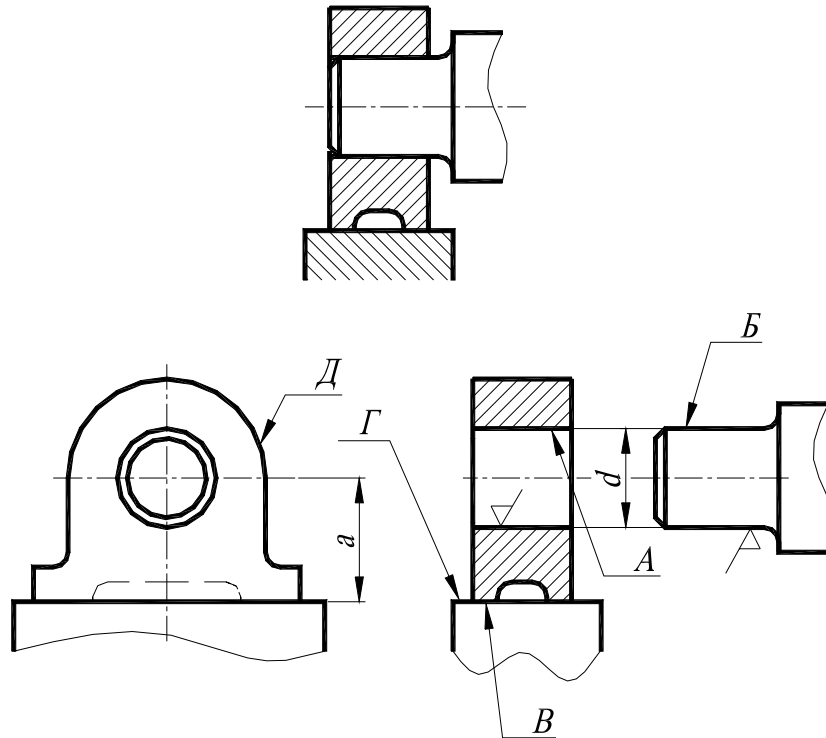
Чертёж, поясняющий деление поверхностей деталей
